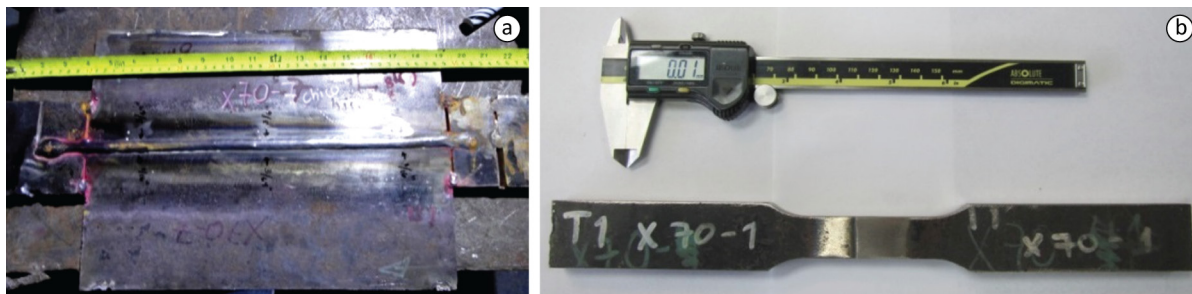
Cupón de prueba soldado (a) y muestra para prueba de tensión (b).
